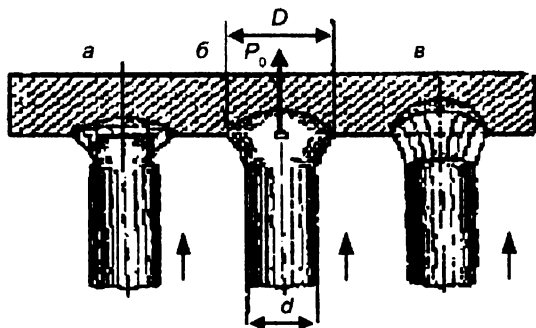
Схема переноса электродного металла через дугу при сварке в потолочном положении
